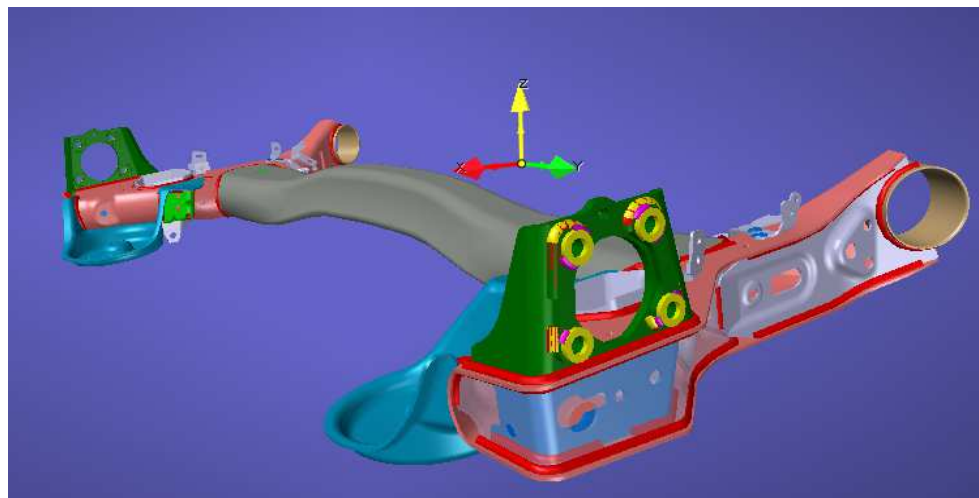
Suporte de roda soldado ao eixo traseiro do veículo
